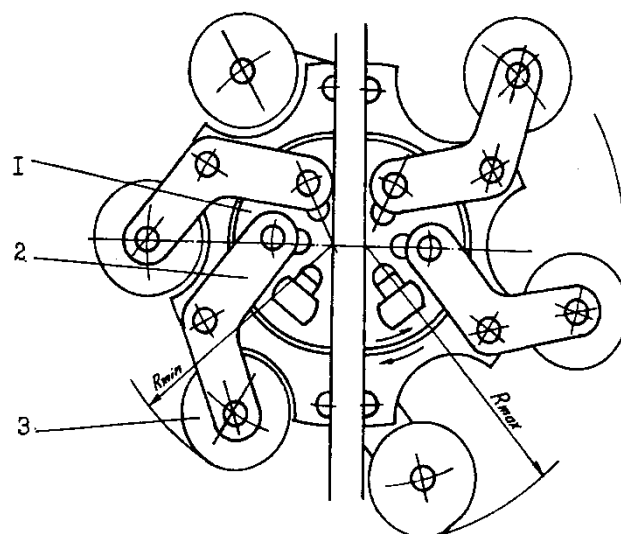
Рабочий орган для уплотнения грунта по а.с. СССР № 894063
